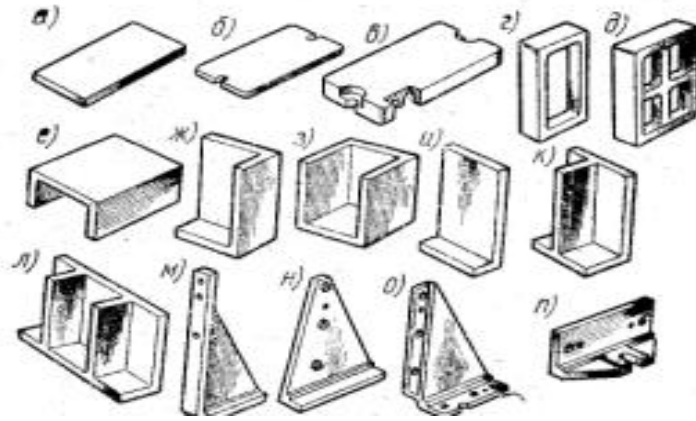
Стандартні деталі (елементи) корпусів: а – плити сталеві, б, в – плити чавунні, г, д – коробки, е – швелери, ж – тригранники, з – чотиригранники, і – кутники, к, л – кутники з ребрами, м, н, о – ребра, п – планки
